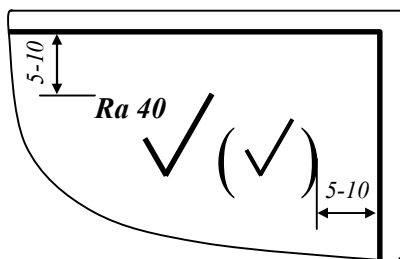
Обозначение шероховатости поверхностей в правом верхнем углу чертежа
